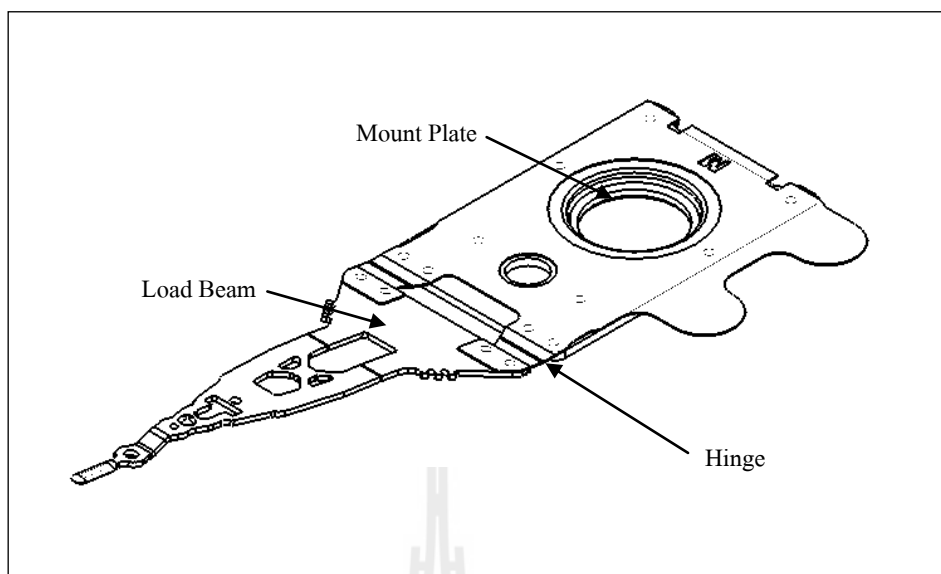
Drawing แบบจำลองของ Load Beam
